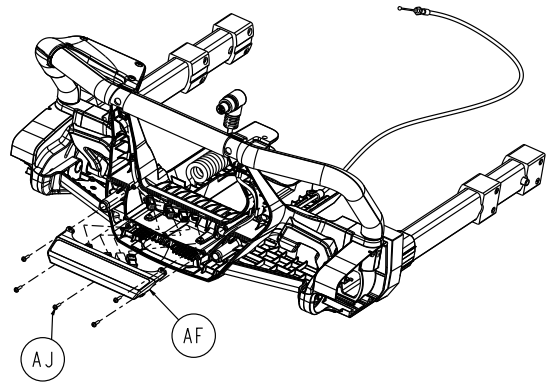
Retirer l'ensemble de câble du module d'éclairage
